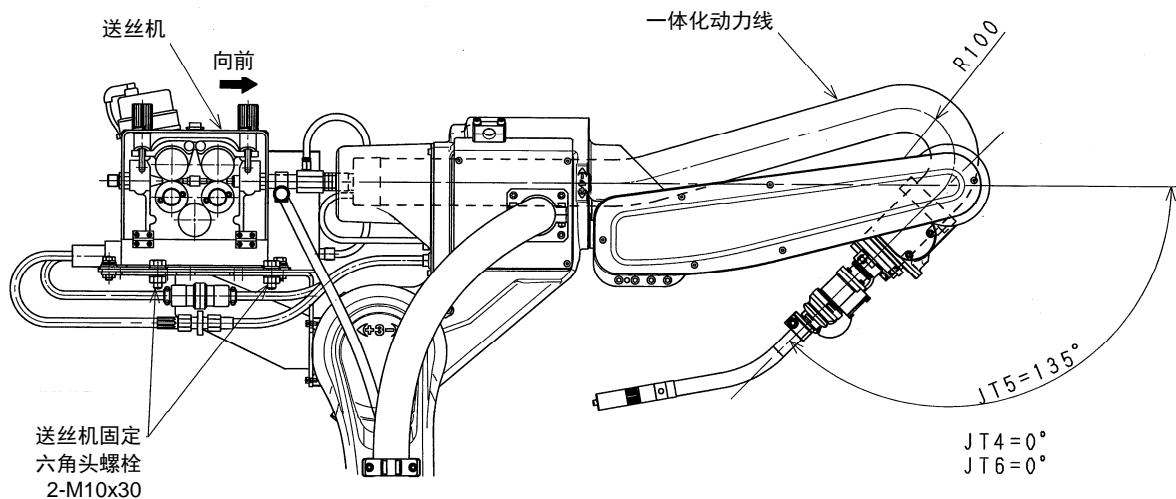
TOKIN 公司生产的焊炬及震动传感器单元的安装(N-type)
